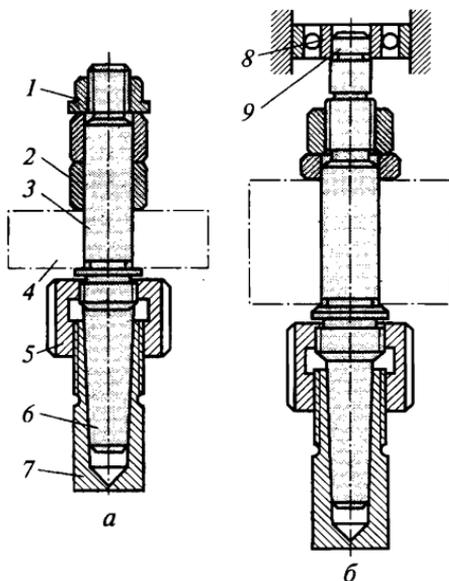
Крепление фрезы на оправке фрезерного станка:
